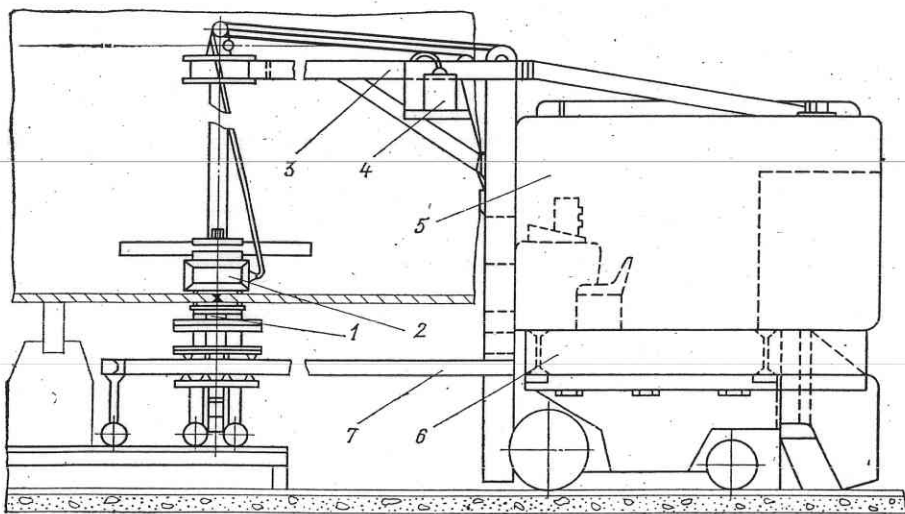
Установка для рентгеновского телевизионного контроля сварных швов:
